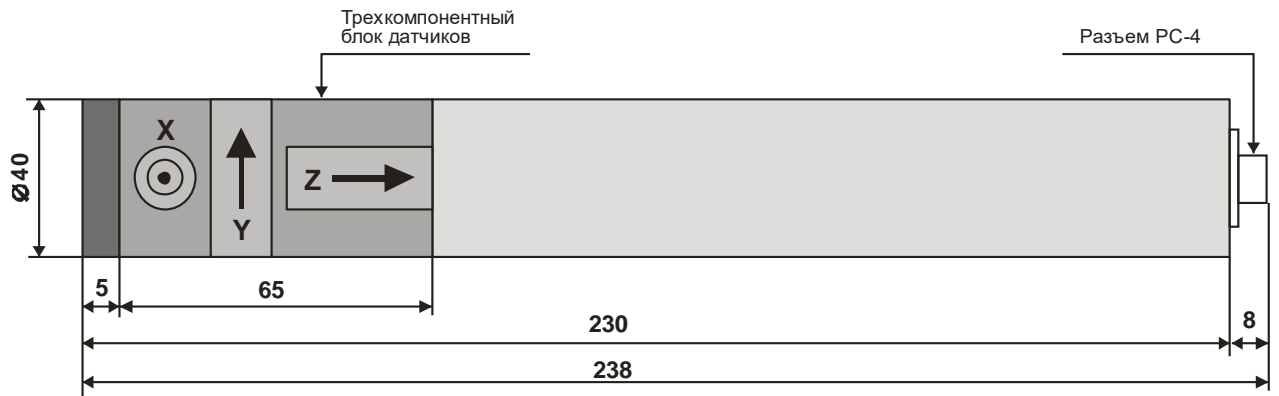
Конструктивный чертеж прибора НВ0302.9А
